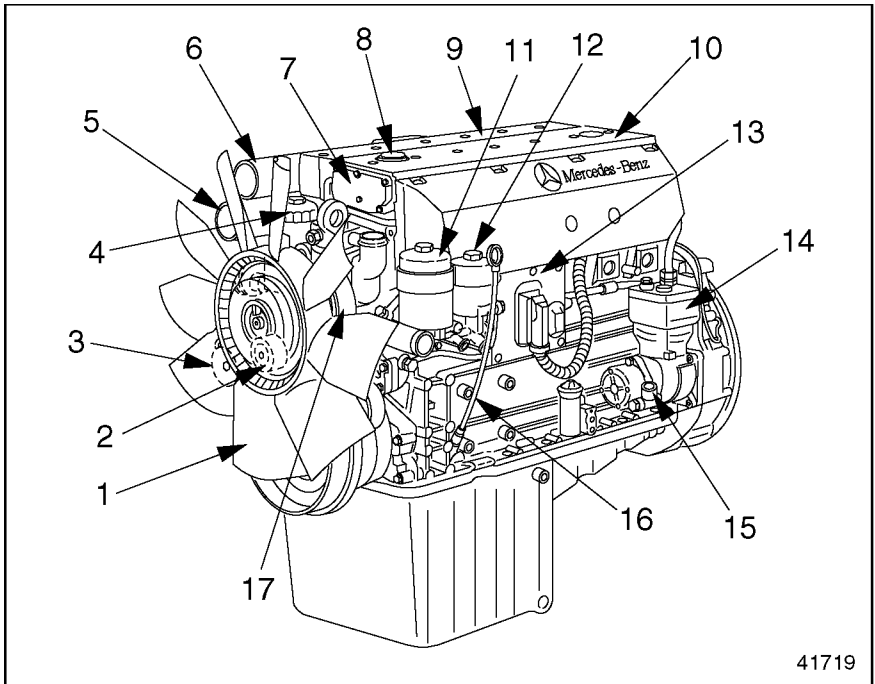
Vista Frontal Derecha del Motor MBE 900 EGR
